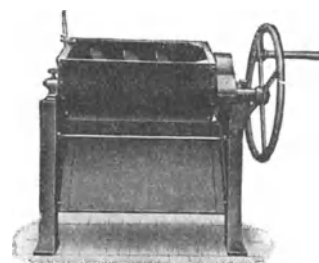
Kernsandmischmaschine mit Schraubenflügeln.
